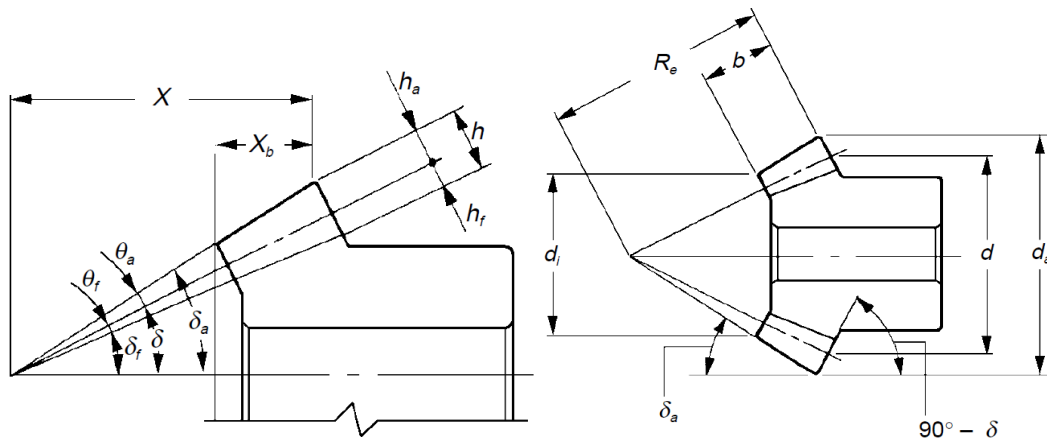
Dimensiones características de los engranajes cónicos de dientes rectos [Kohara Company].
